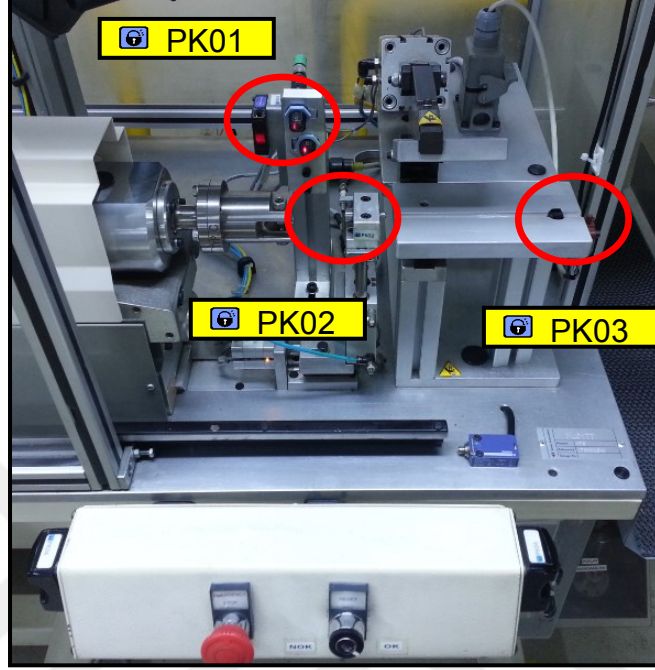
Spinwelding makinasının üzerindeki sensörler
